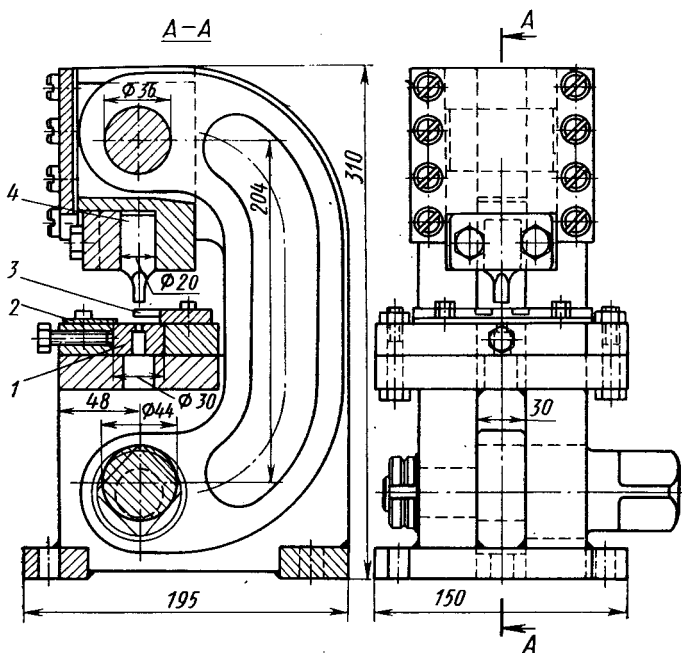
Портативный пресс для пробивки отверстий для шипов лопаток в бандажных лентах:
